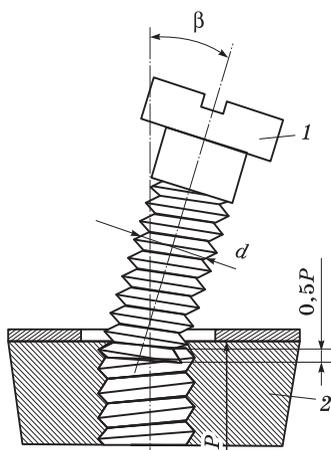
Перекос осей при сборке двух резьбовых деталей
